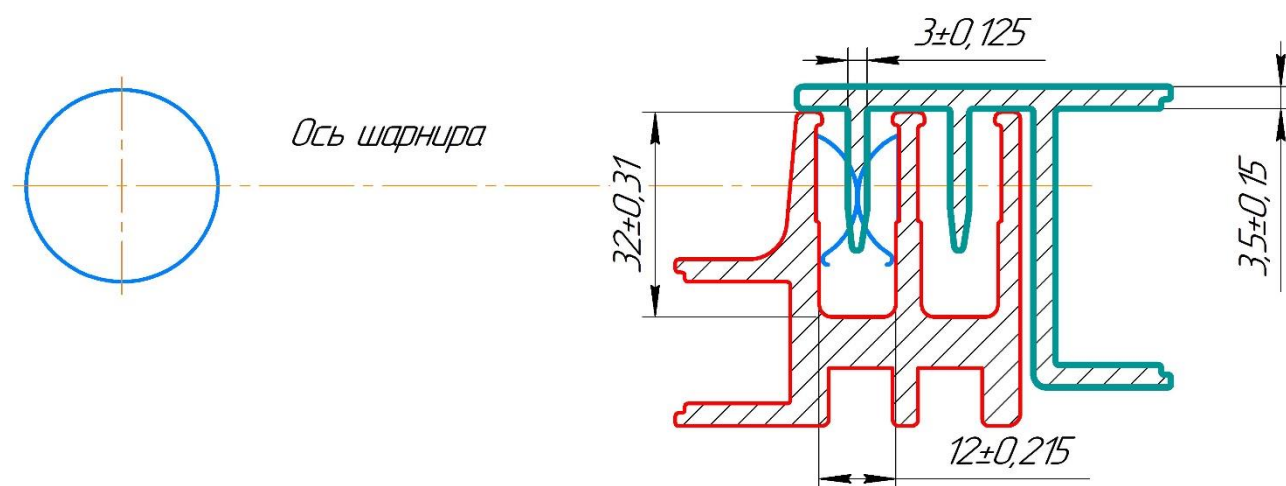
Предлагаемый вариант размеров профиля стены и короба двери
